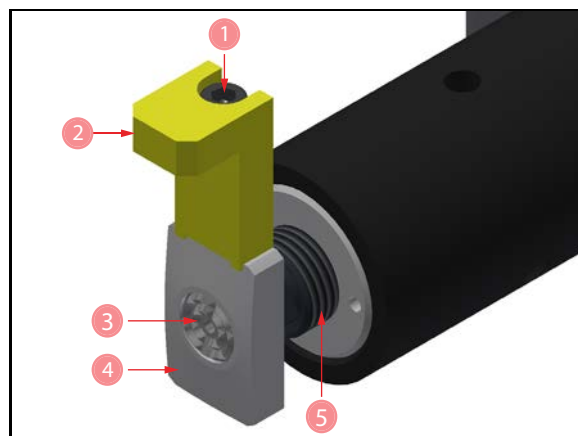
COMPOSANTS STANDARD DE LA JAMBE DE SERRAGE DI
